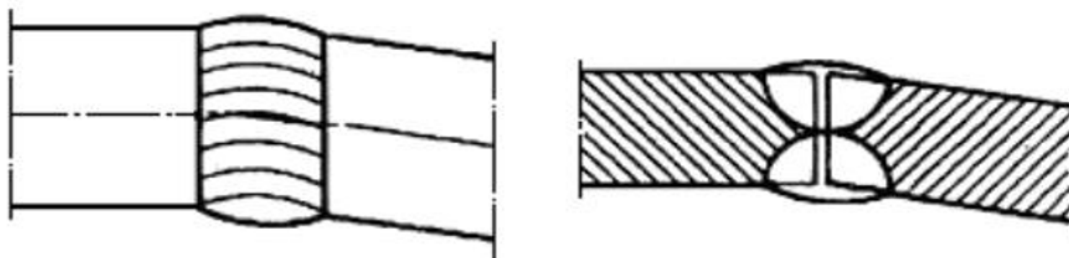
Эскиз дефекта сварного шва
